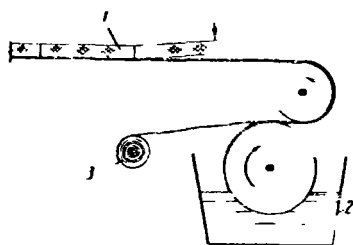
Схема склеивания полистирольных плит с рулонным кровельным материалом
